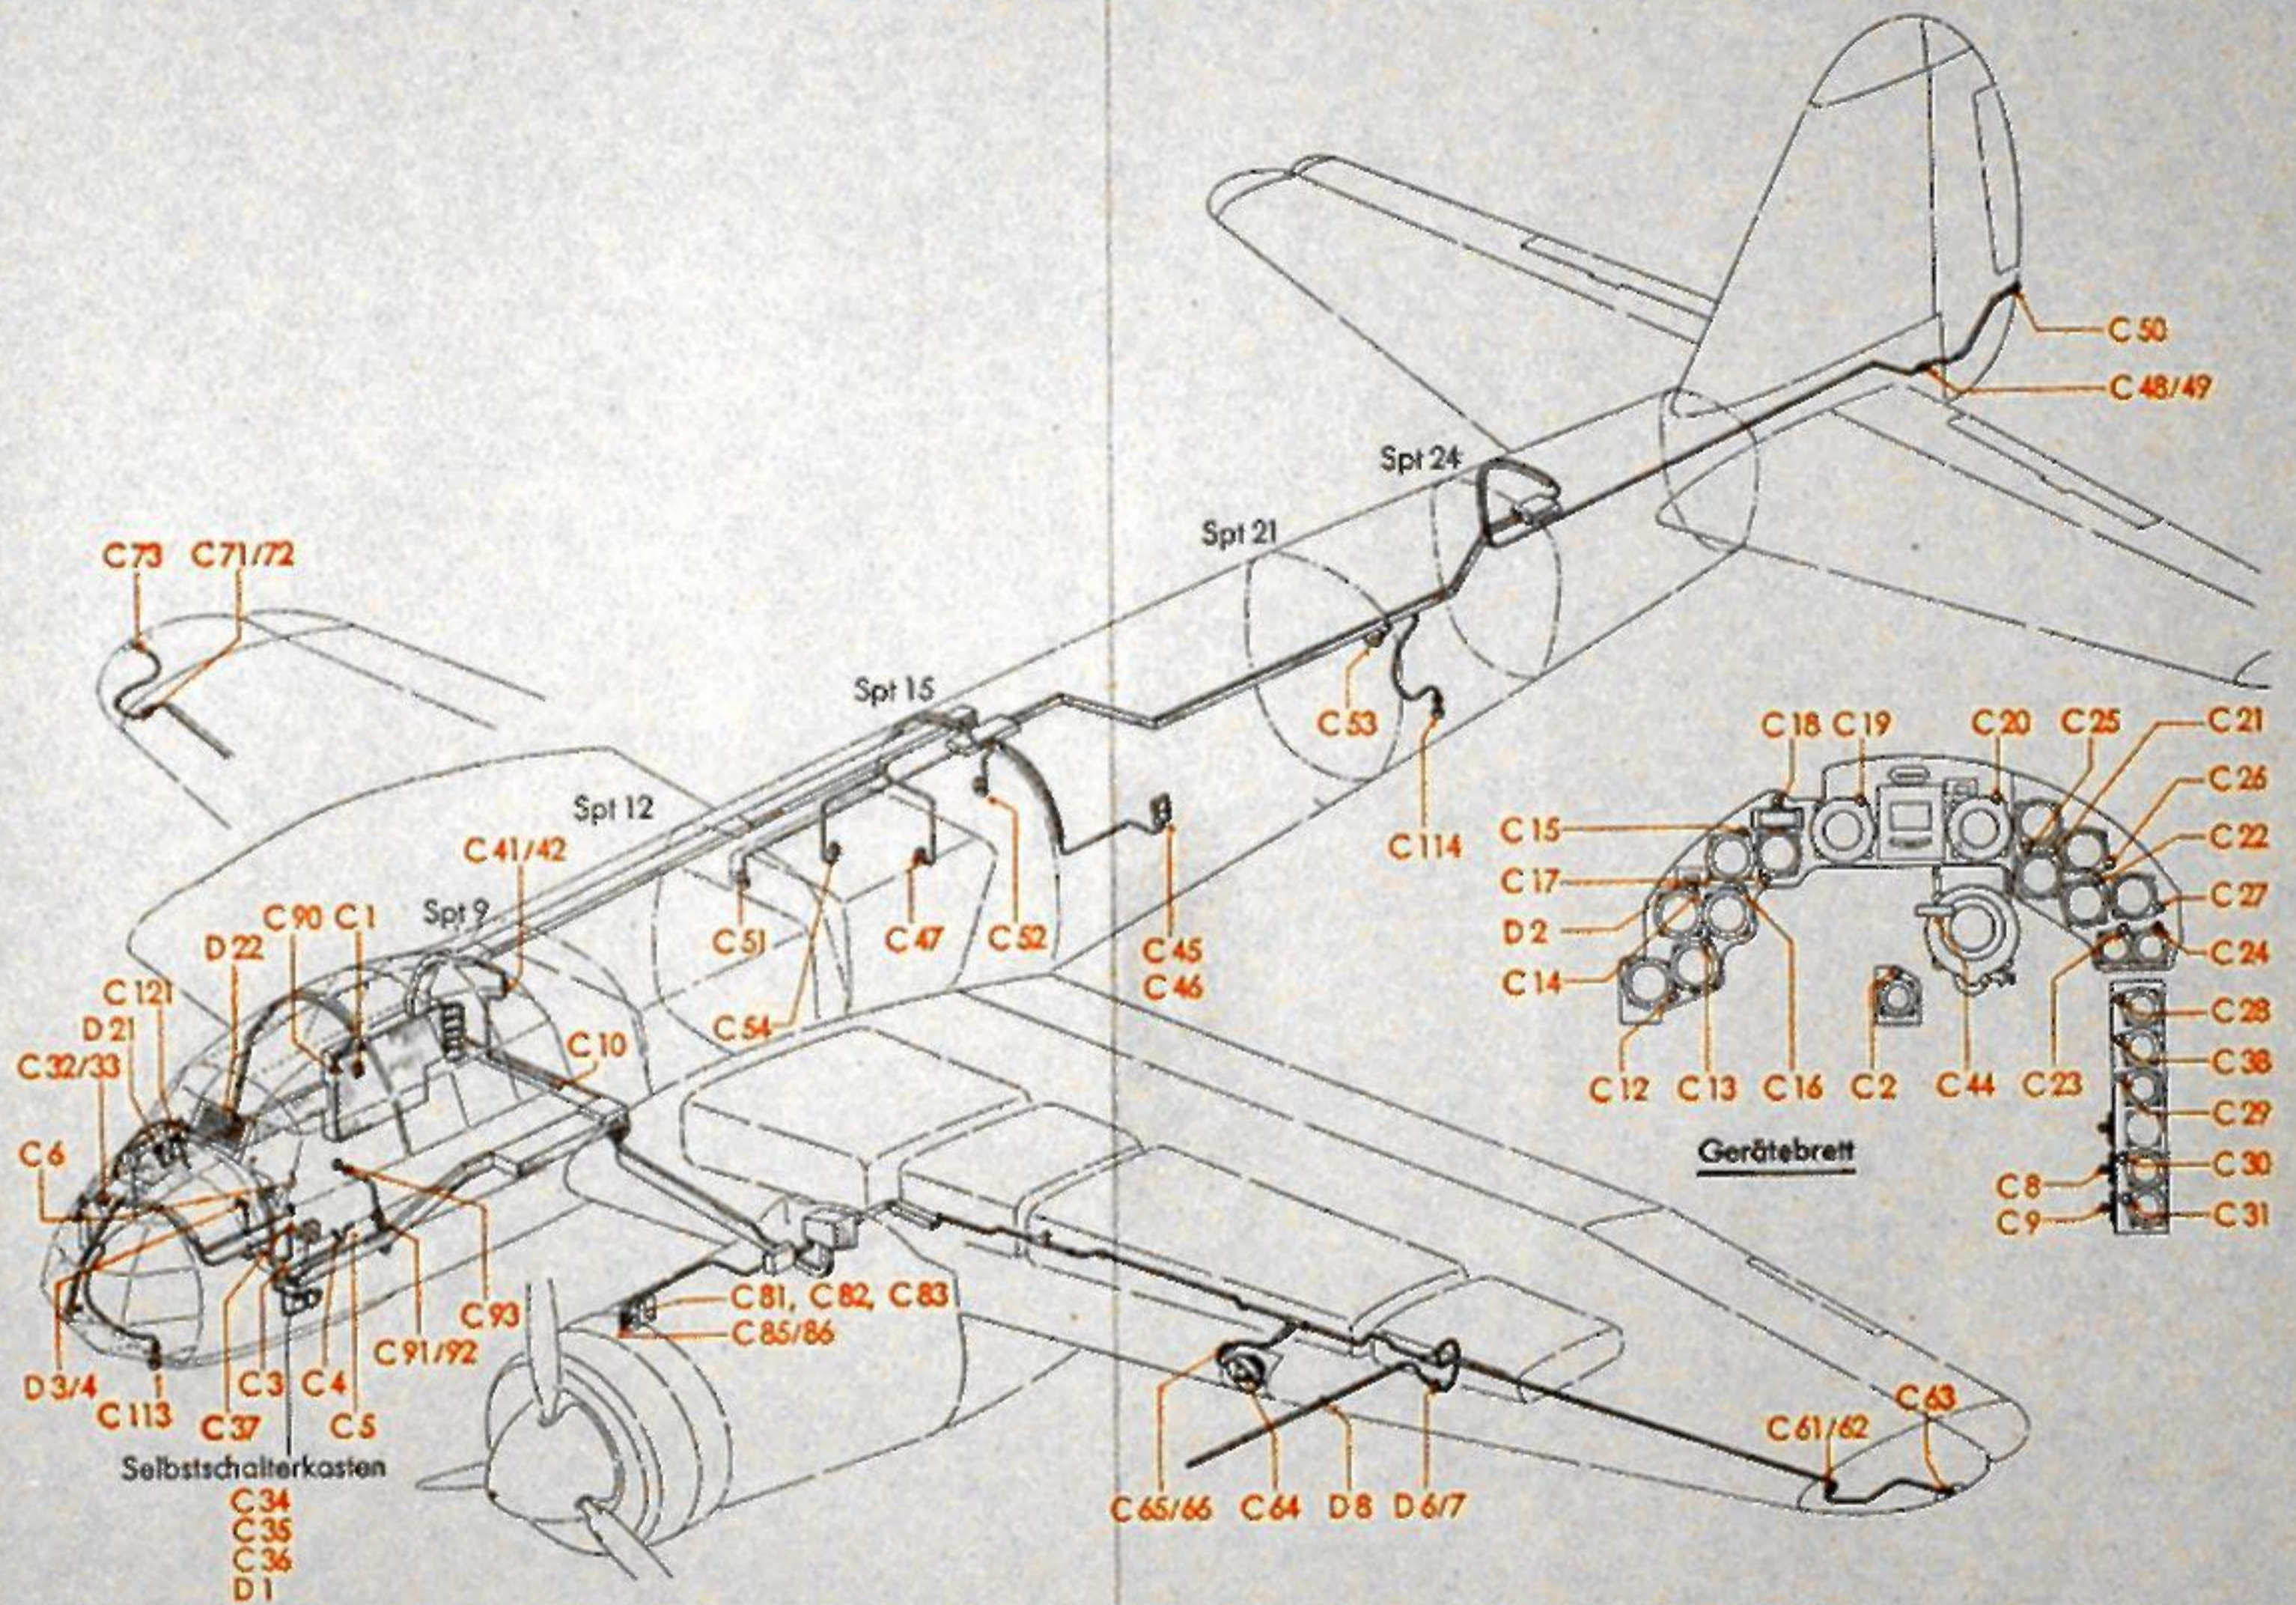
Lageplan der Beleuchtung- und Staurohrheizungsanlage / C- und D-Anlage
